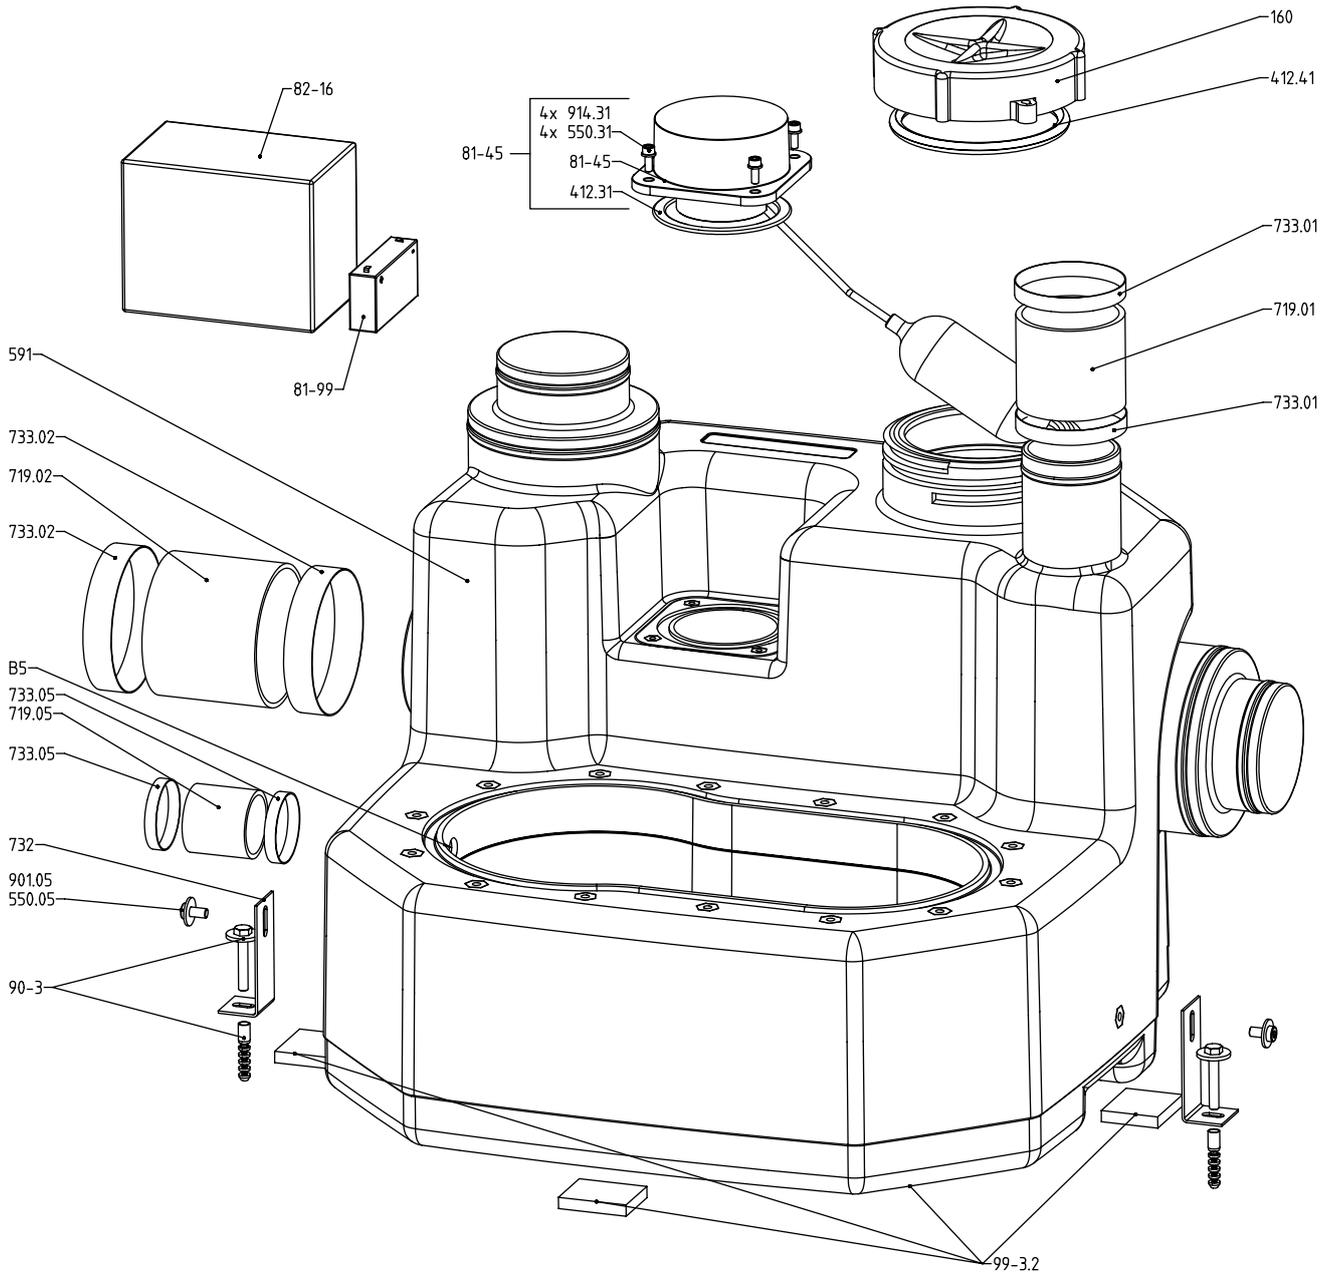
Деталировочный чертеж mini-Compacta US100 - сборный резервуар
